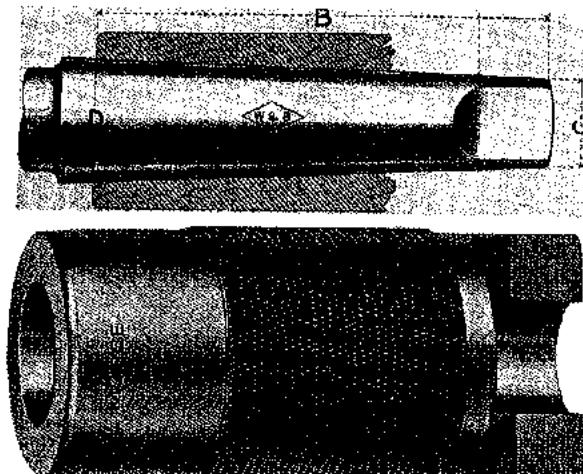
Mango cónico y calibre cónico de anillo (Morse Twist Drill & Machine Co. y Whitman & Barnes).
